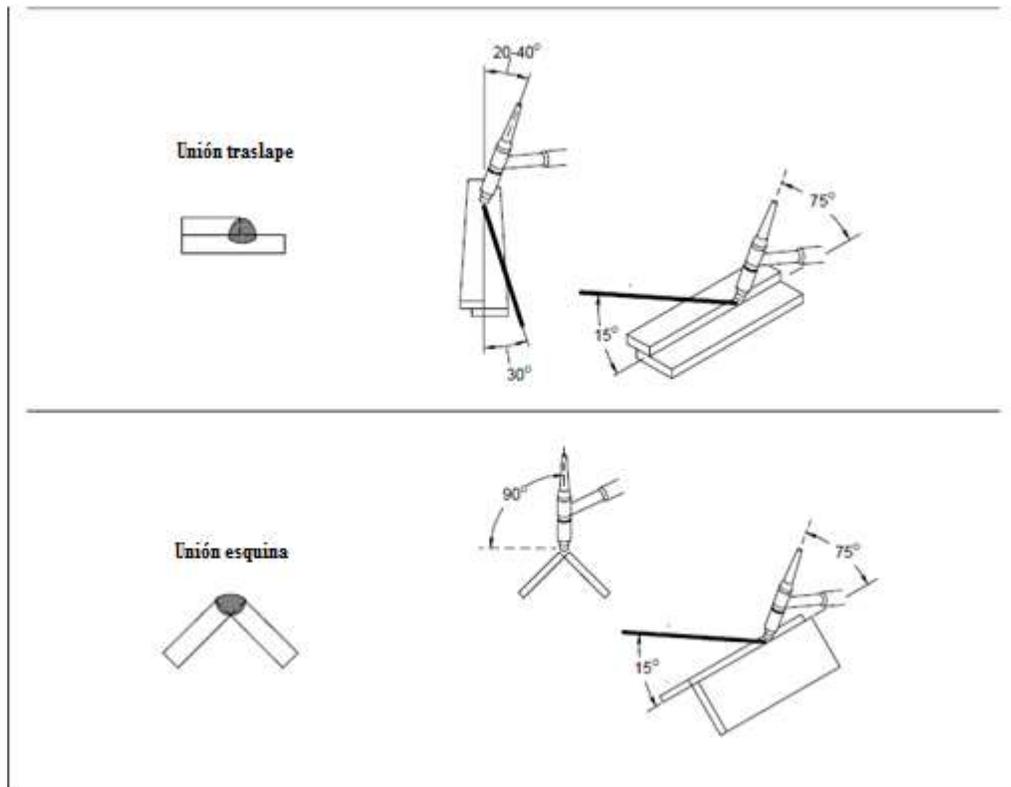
Diferentes tipos de uniones para soldadura TIG.
